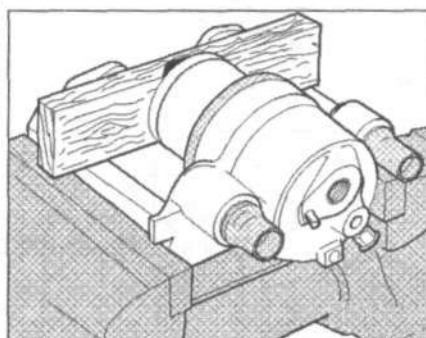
Извлеките поршень из тормозного суппорта с помощью сжатого воздуха.
